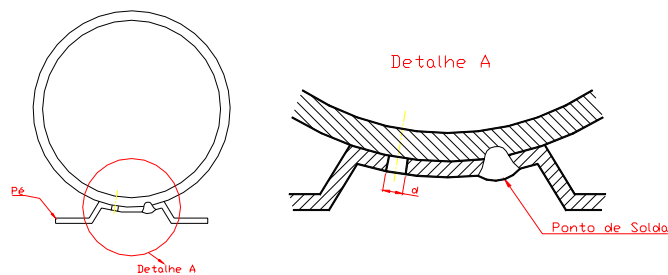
Desenho esquemático dos pontos a serem soldados
